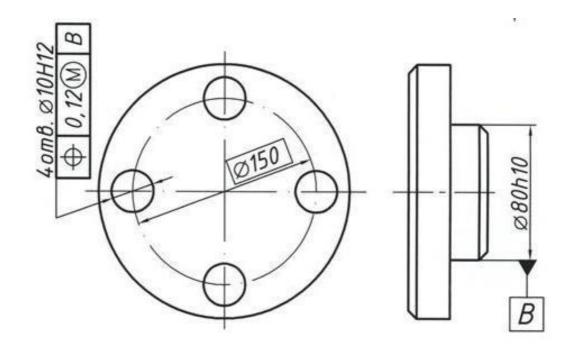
Чертеж контролируемой детали с базовым элементом в виде цилиндра
